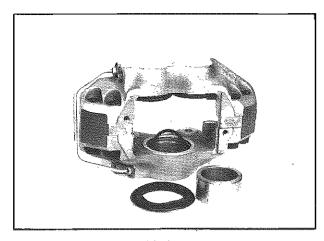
Montare nuove guarnizioni Fitting new gaskets
